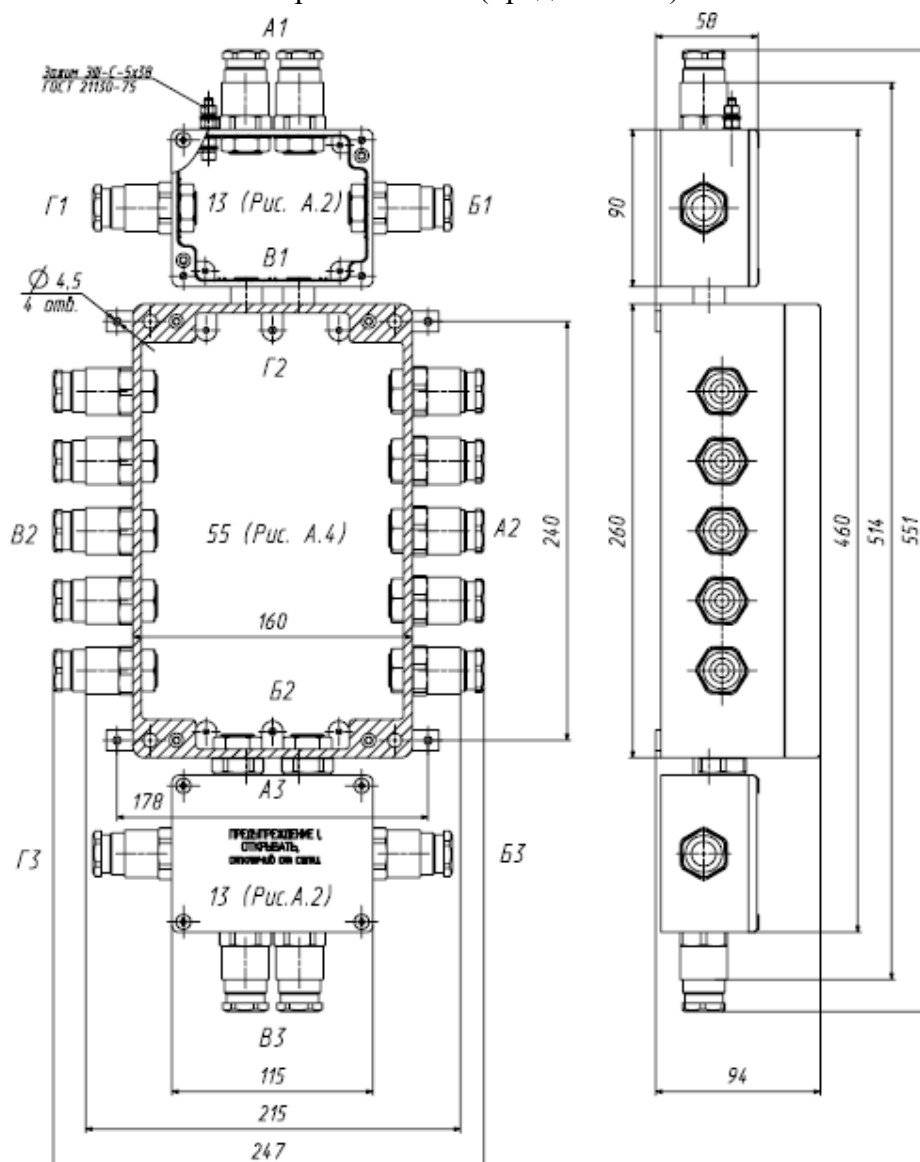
Блок корпусов и коробка клеммная ЕхБКО- А13В1/А55Г2Б2/А13А3 (скрепление корпусов типоразмеров 13, 55 и 13 сторонами В1-Г2, Б2-А3) – вариант 11
